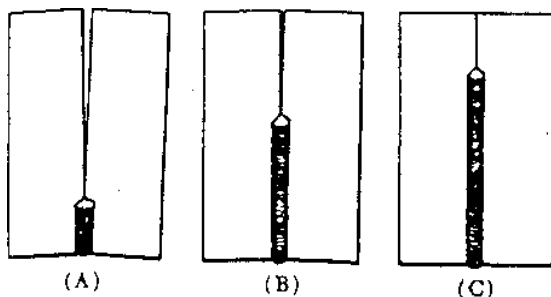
Tolerância para a soldagem de topo em chapas de aço.
